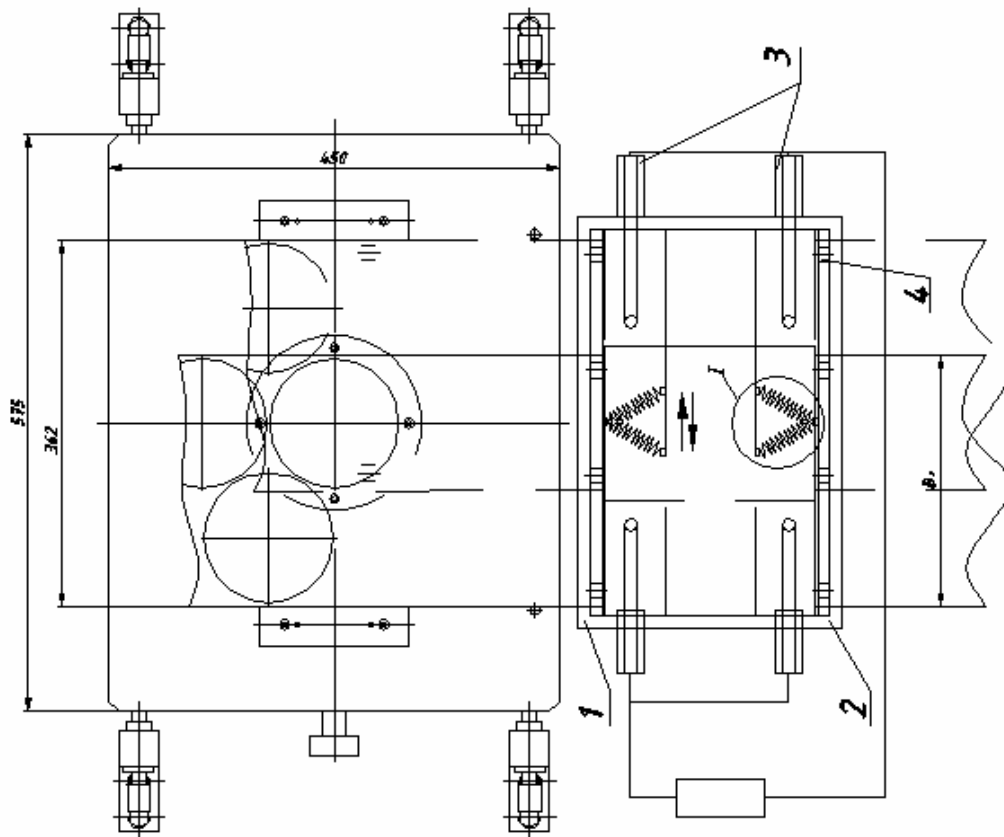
Устройство к многопозиционному прессу для подачи ленточного материала (вид сверху)
